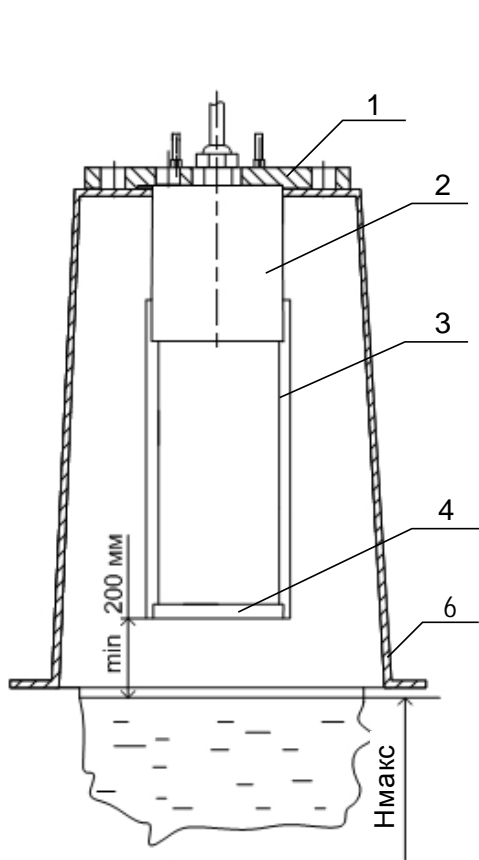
Установочный патрубок для АС-81х-110, АС-90х-110.
